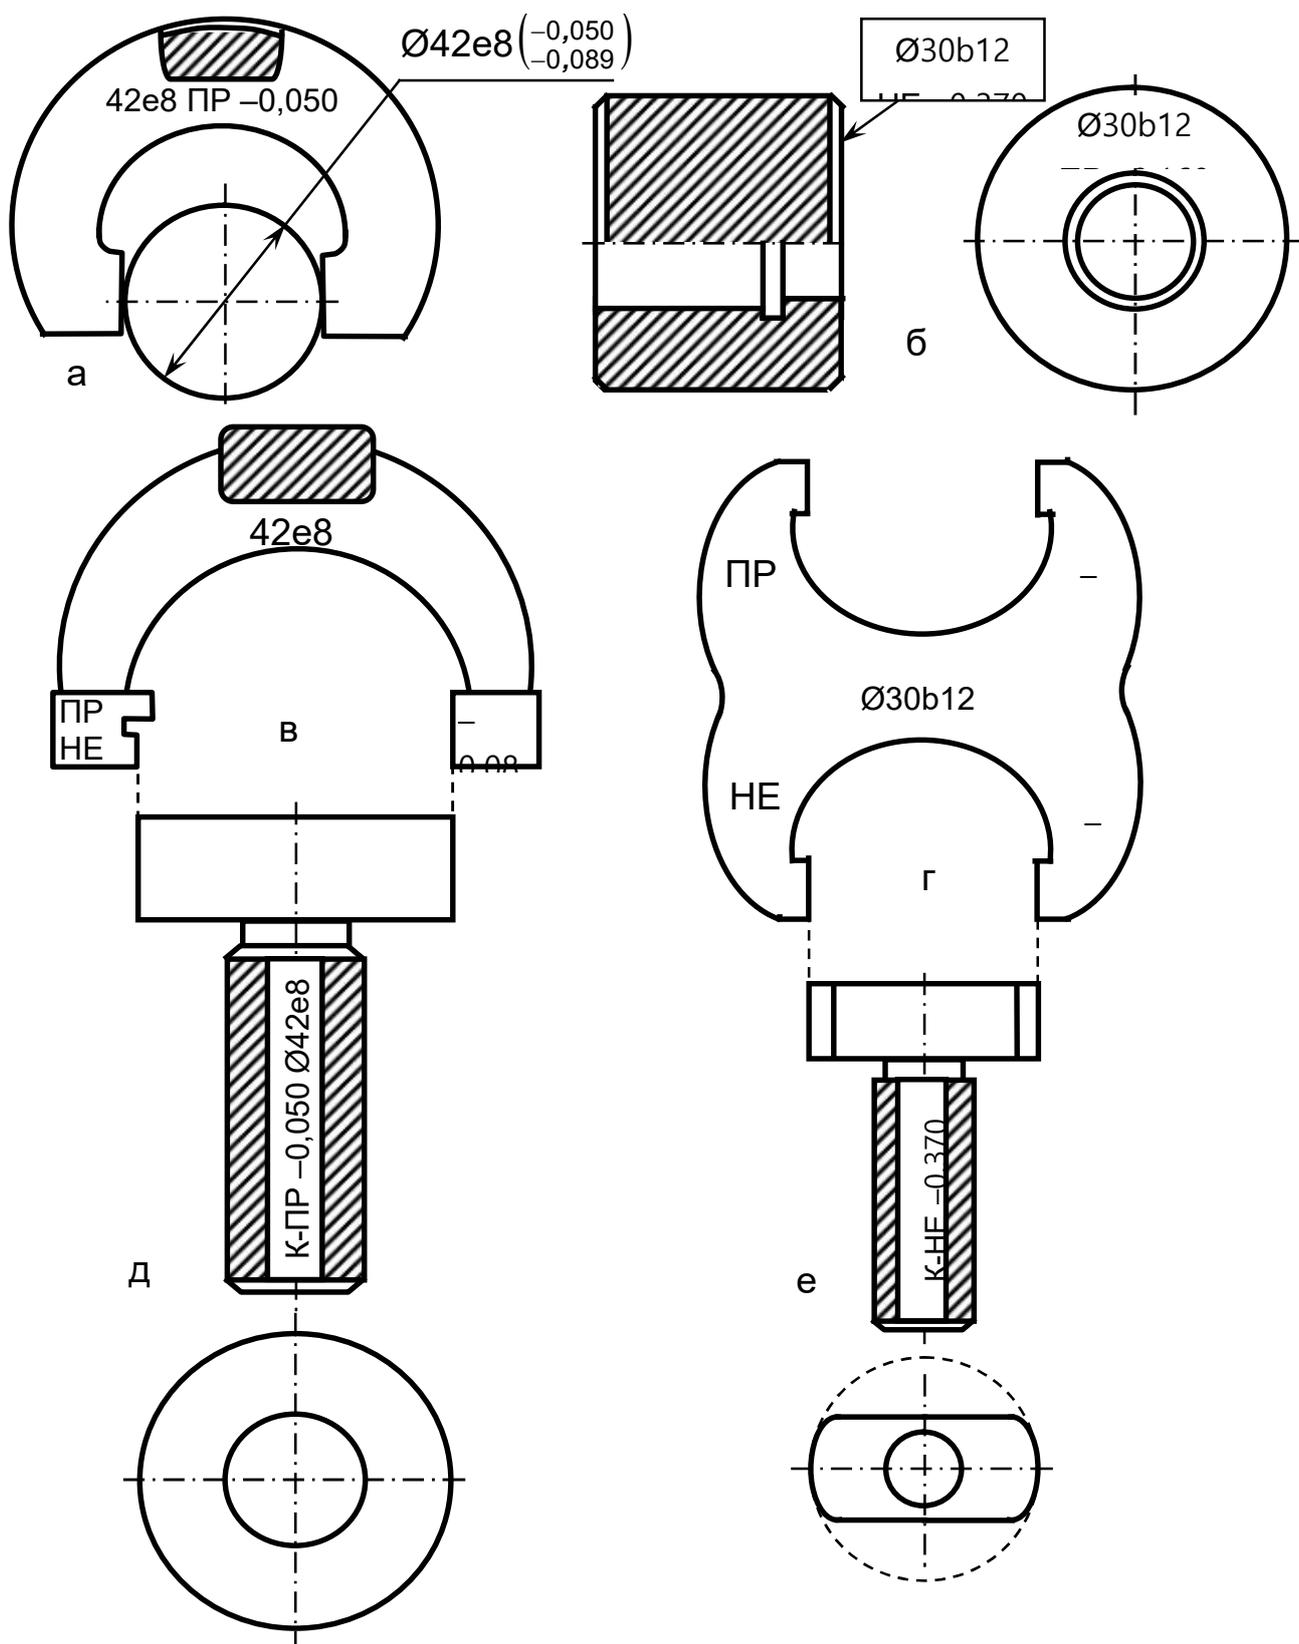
Конструкции рабочих и контрольных калибров: а – однопредельный односторонний рабочий калибр-скоба с проверяемой деталью (вал); б – двухпредельный односторонний рабочий калибр в форме кольца; в – двухпредельный односторонний рабочий калибр-скоба; г – двухпредельный двухсторонний рабочий калибр-скоба; д – контрольный калибр в форме вала (пробки); е – контрольный калибр в форме усеченного вала
